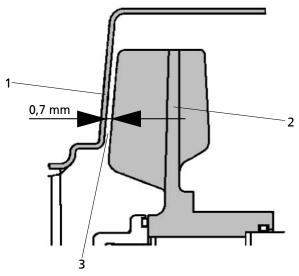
Axialspalt zwischen Pumpengehäuse und Laufrad
